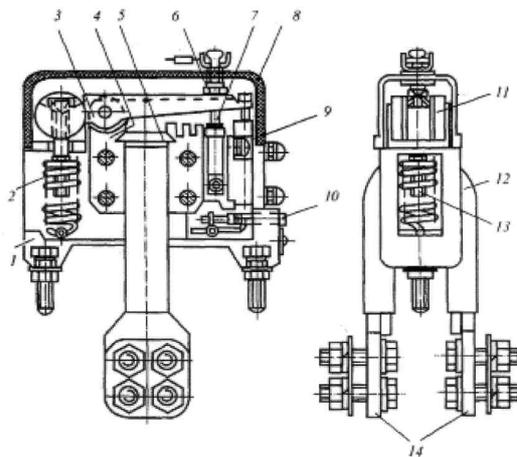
Реле токовой перегрузки РТ: 1 - изоляционная боковина; 2 - отключающая пружина; 3 - якорь; 4 - П-образный магнитопровод; 5 - клин; 6 - гайка; 7 -ограничительная шпилька; 8 -пластмассовый кожух; 9 - блокировочное устройство; 10 -указатель срабатывания; 11 - противовес; 12 - полвитка шины (катушка); 13 -регулирующий болт; 13 - выводы шины.
